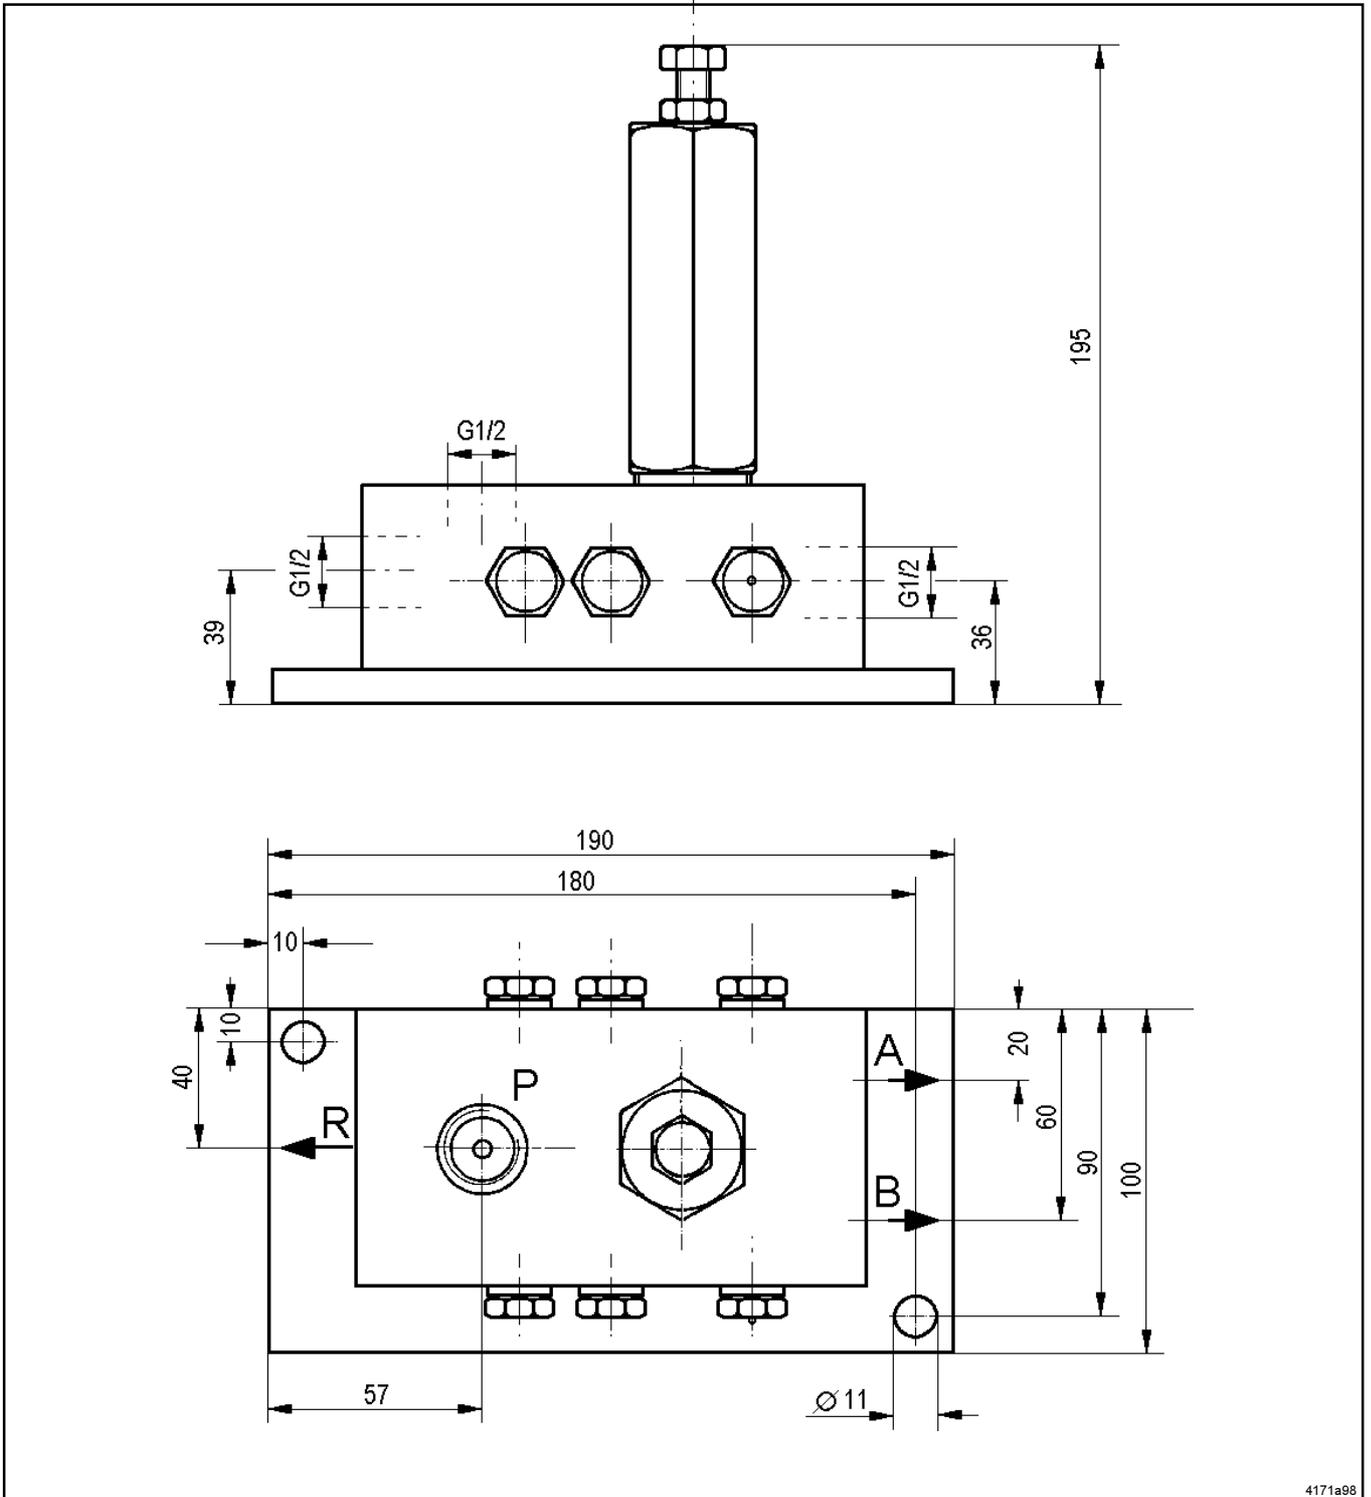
Vanne d'inversion DU1-GK (n° réf. 617-28619-1) sur plaque de base, avec tige de contrôle
